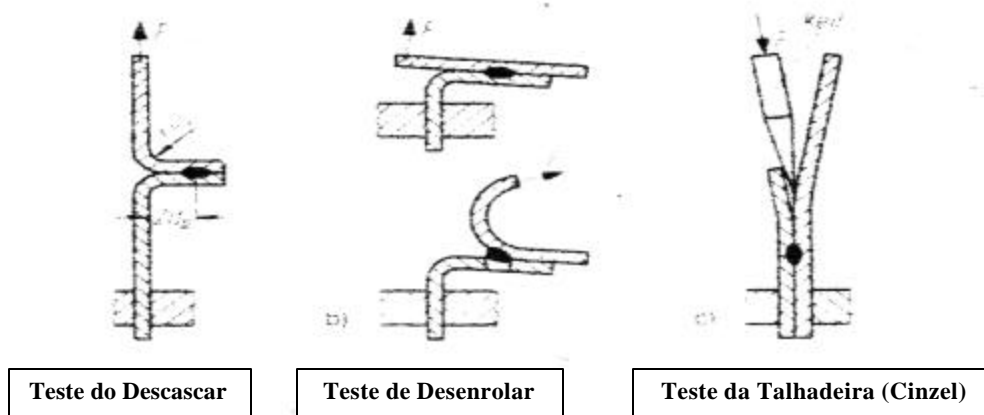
Testes para medir o diâmetro do ponto soldado.
